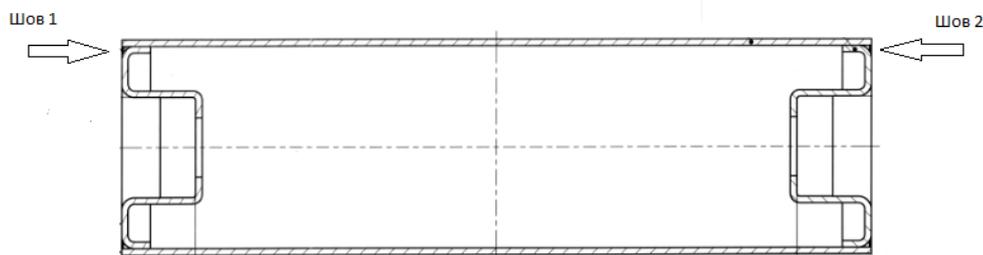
Схема сварки корпуса ролика ленточного конвейера
